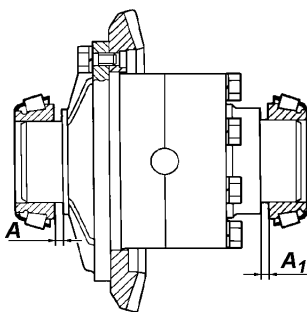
Зазоры A и A_1 между торцами подшипников и коробки сателлитов
